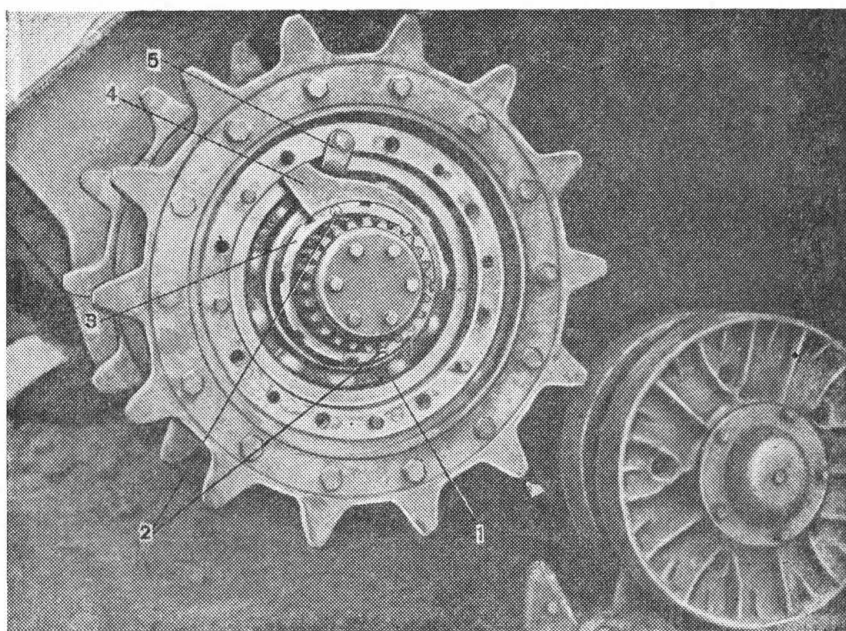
Отвертывание гайки крепления ведущего колеса:
